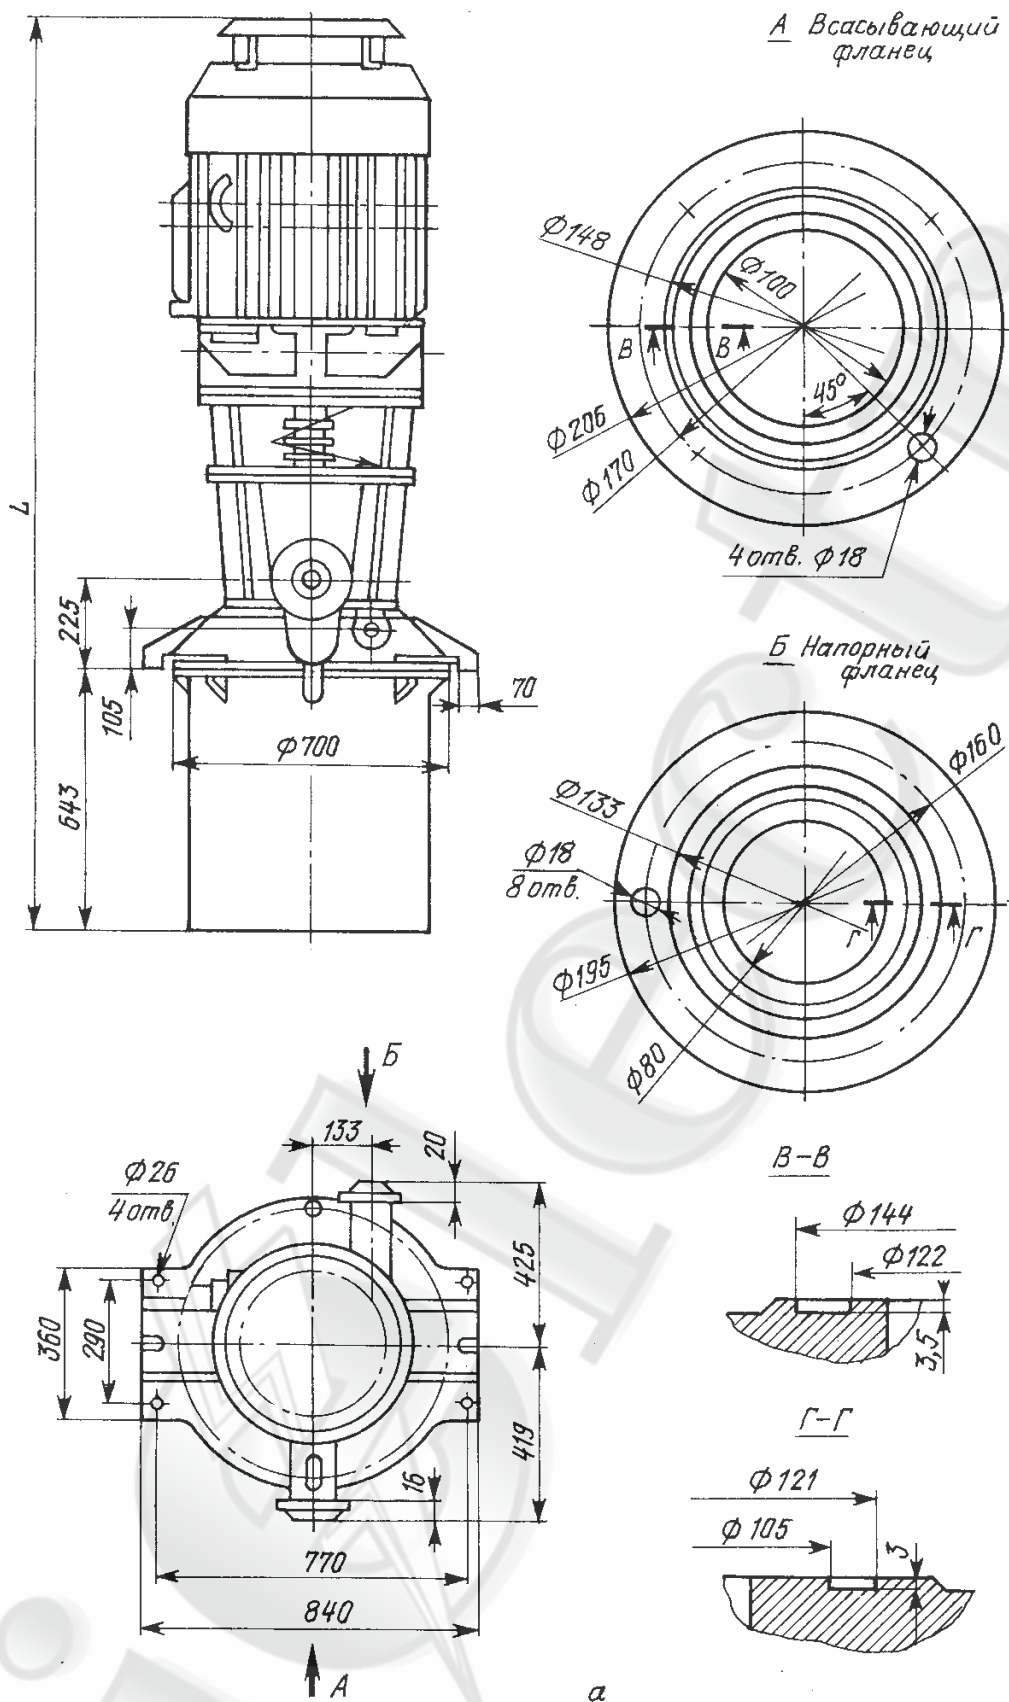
а. Общий вид, габаритные, присоединительные размеры и масса агрегата для различных типов комплектующего электродвигателя
